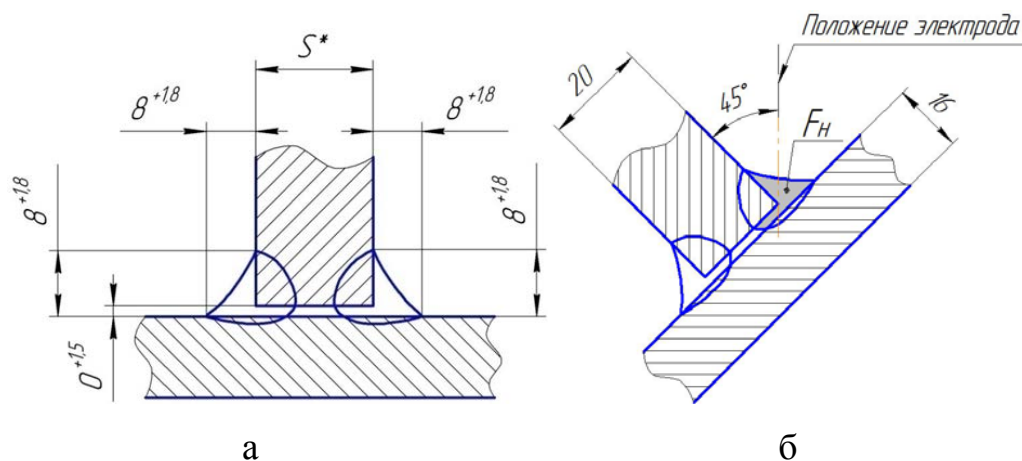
Эскиз сварного шва № 2 (а) и расчетная схема(б)
